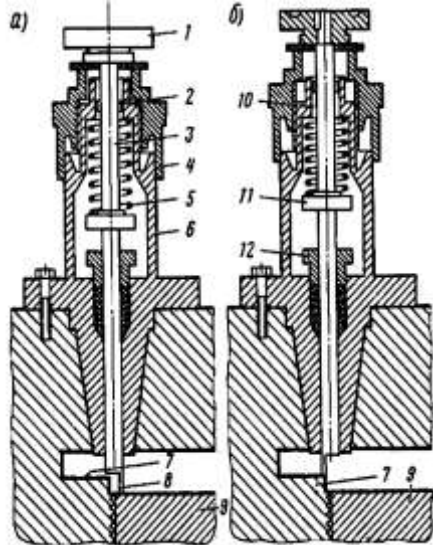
Приспособление для оживления шейки при выкатывании вкладыша
